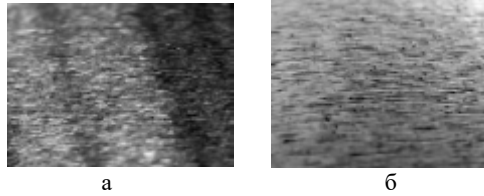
Обробка лопатки компресора після ручного полірування
